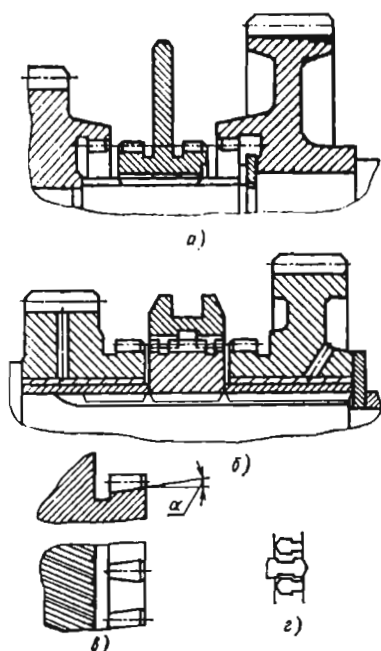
Виды зубчатых муфт и их зубьев:
